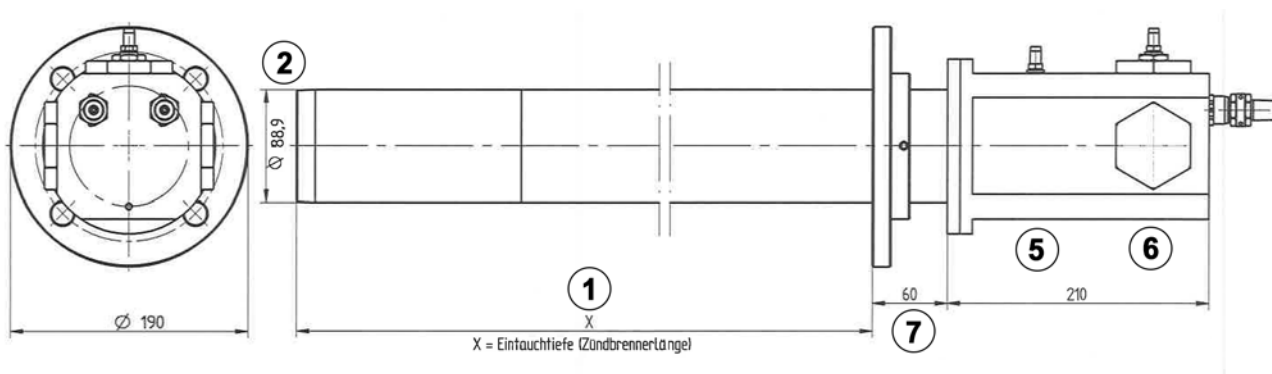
Dimensões do queimador de ignição GF189 modelo C
